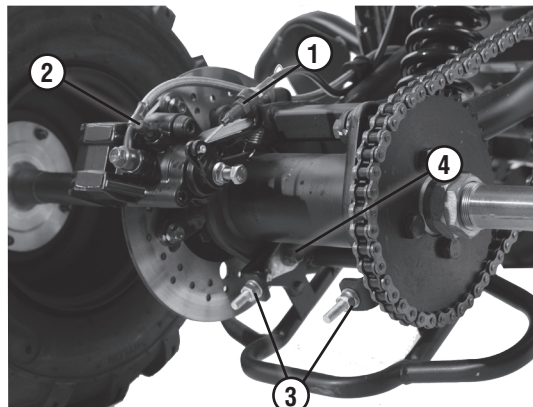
Дисковый тормоз задних колес и регулировка натяжения цепи
